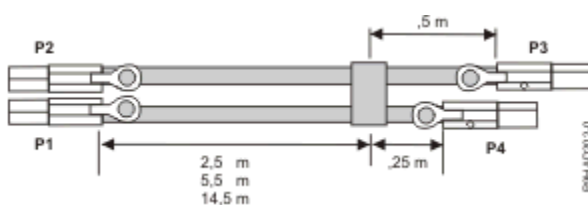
Comprimentos de cabo de montagem de cabo YO externo SAS
